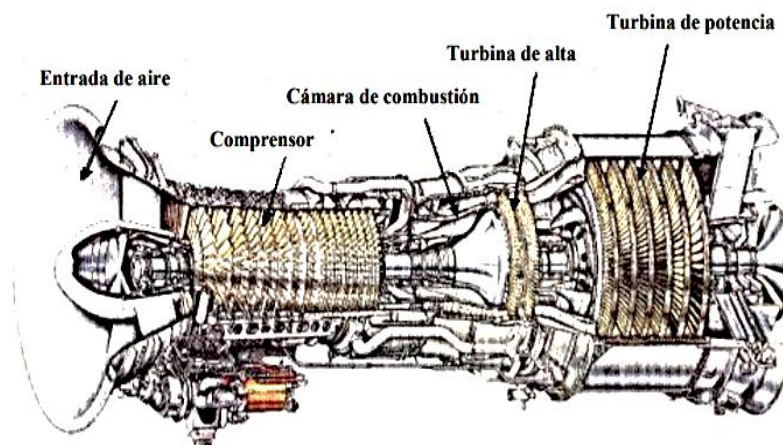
Partes de una Turbina a Gas – Fuente Internet
